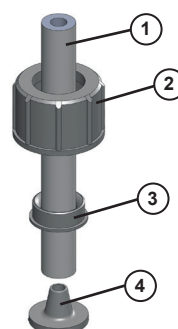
Schlauchklemm-Anschluss 6/12 (Innen- und Außendurchmesser in mm)
